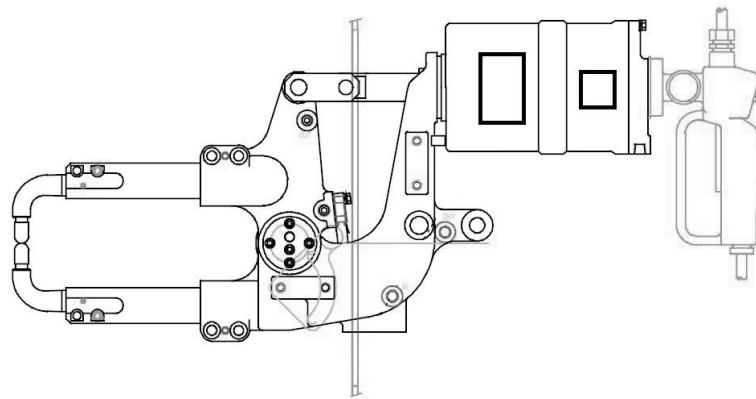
4. Equipo de soldadura por puntos portátil tipo X .
